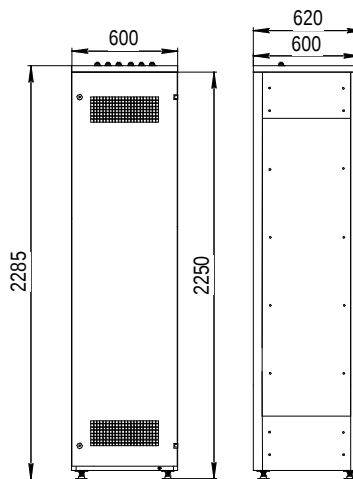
Габаритный чертеж шкафа аккумуляторного СУЭП-2 А1
